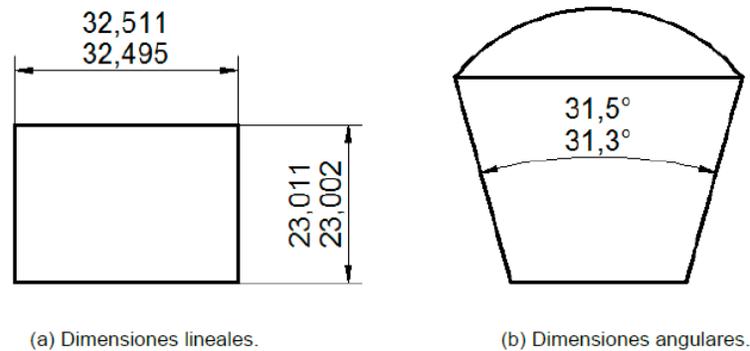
Representación de la tolerancia dimensional.
